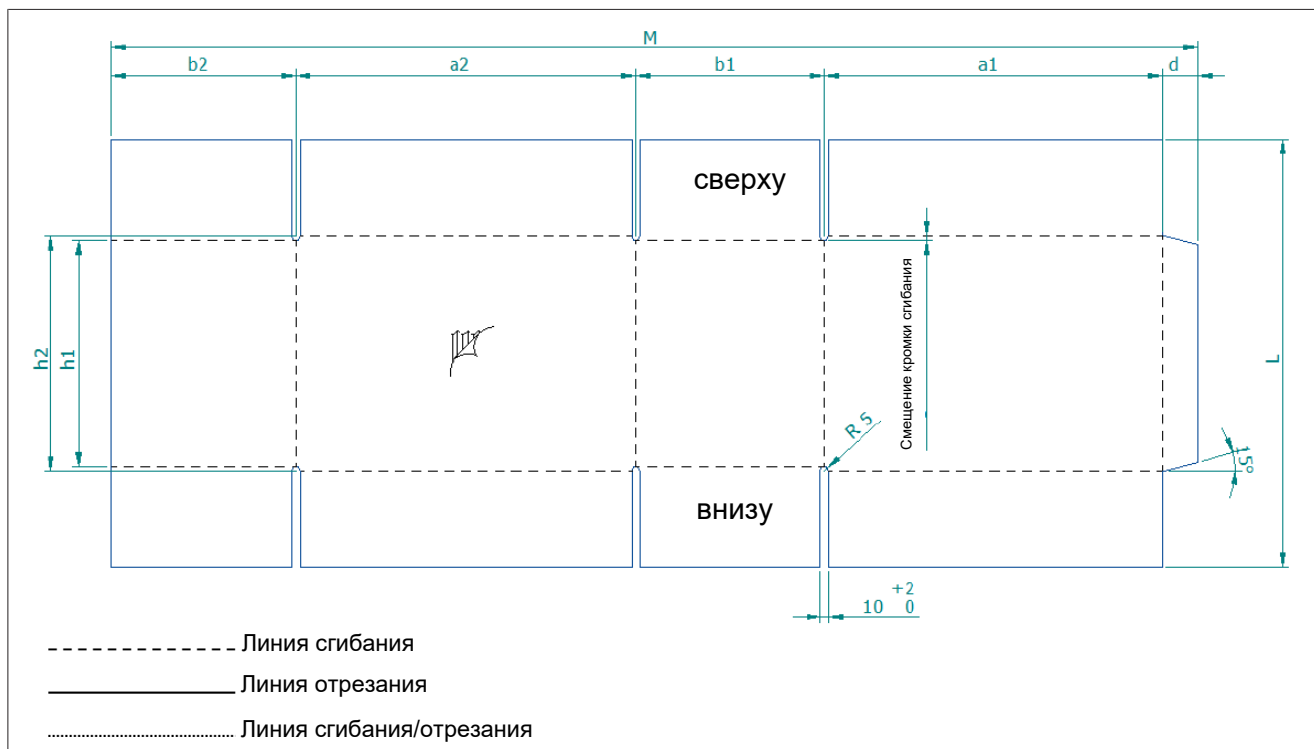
Чертёж предложения Картонная коробка с накладками крышки
